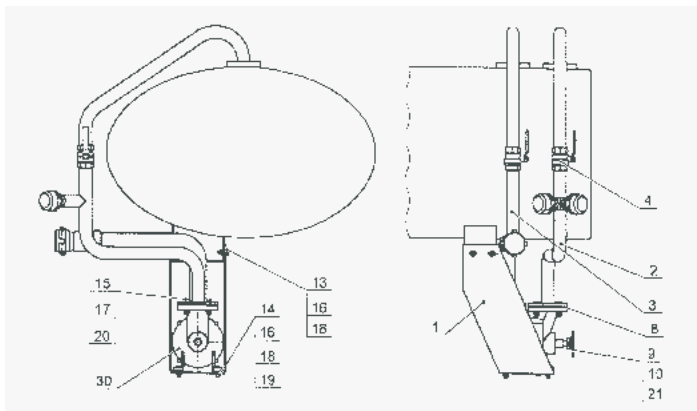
Гидравлическое оборудование APC-14ПМ:
